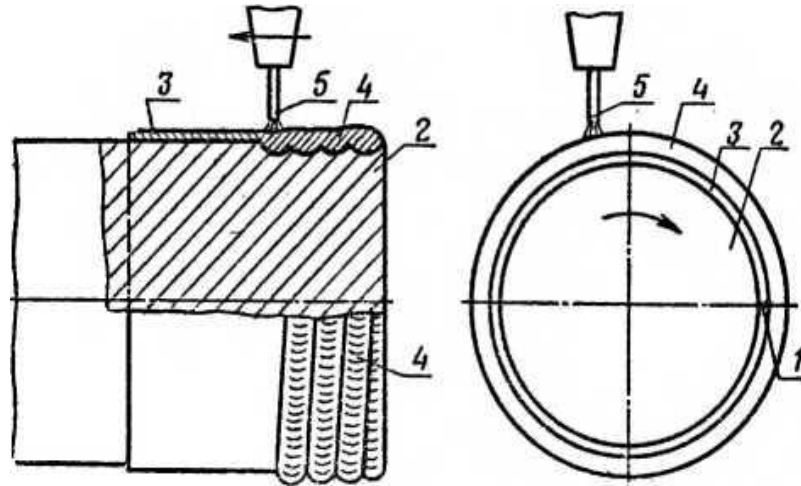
Схема наплавлення шийки валу з металевою оболонкою:
